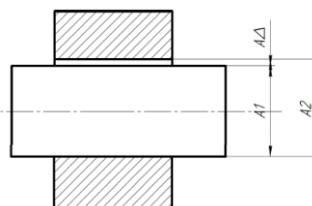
Конструкторская размерная цепь (посадка): A1 – диаметр вала; A2 – диаметр отверстия; AΔ – зазор или натяг в посадке.
